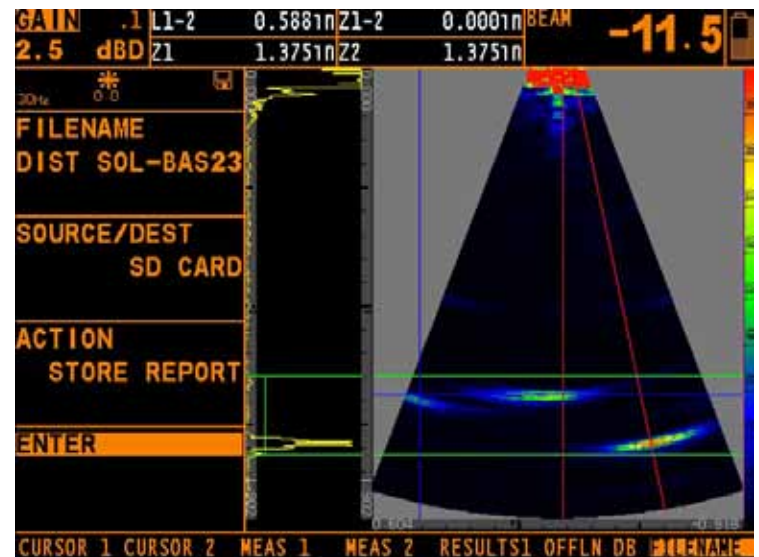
Imagen del Barrido Sectorial con el cursor a -11.5° , tocando parte de la corona de la soldadura.
